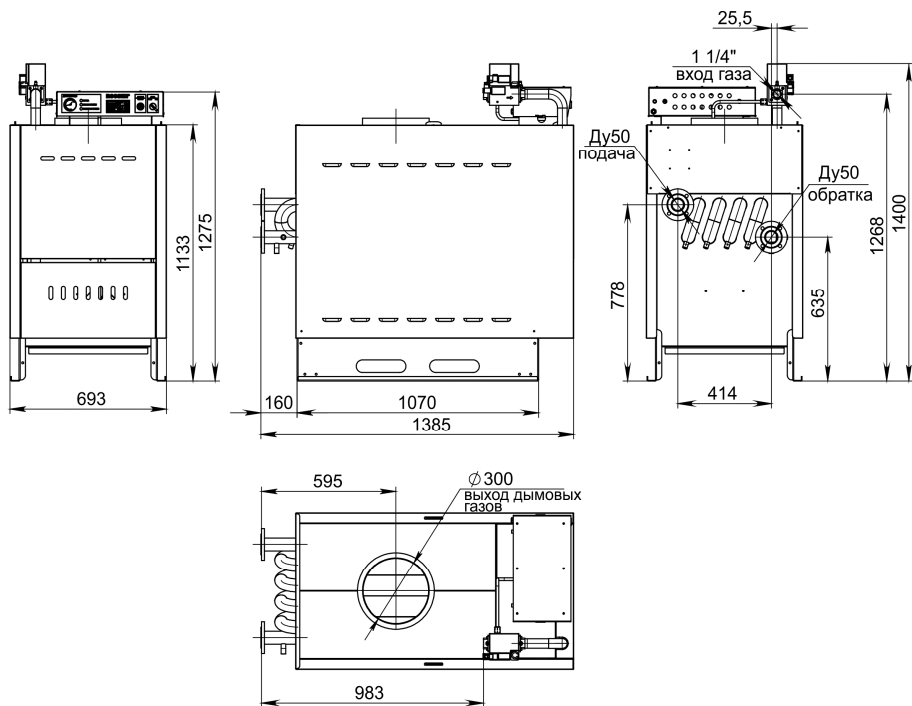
Габаритно-присоединительные размеры котла RSA150
